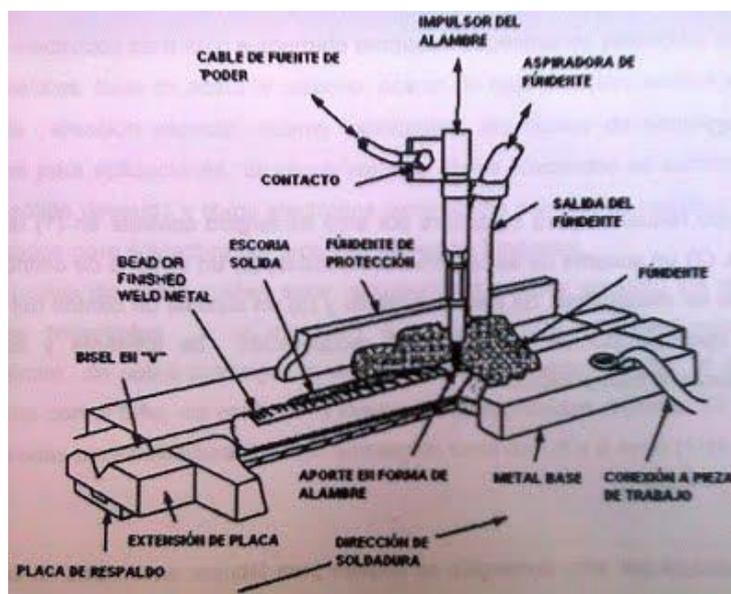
Proceso de soldadura por arco sumergido.
